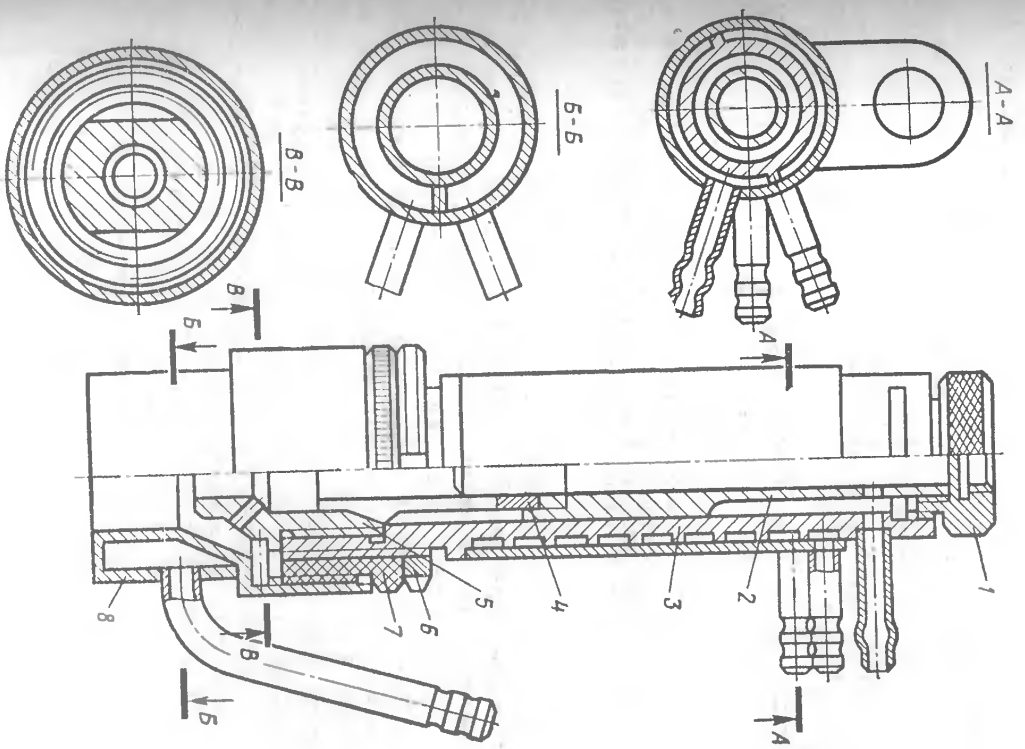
Горелка ИГНА-1000 для механизированной дуговой сварки:
